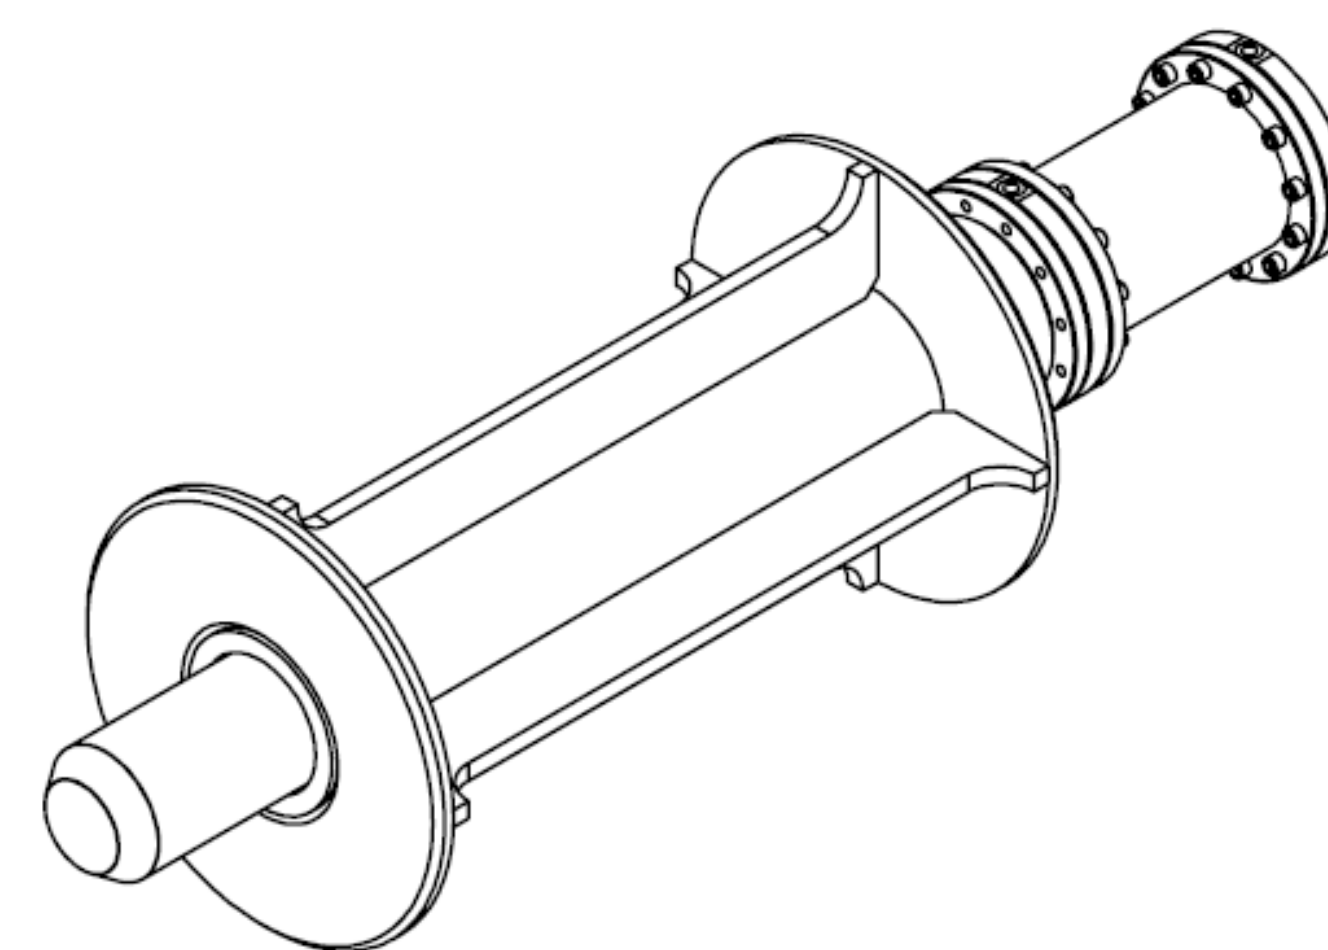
Vista isométrica do desenho de conjunto dos pinos
